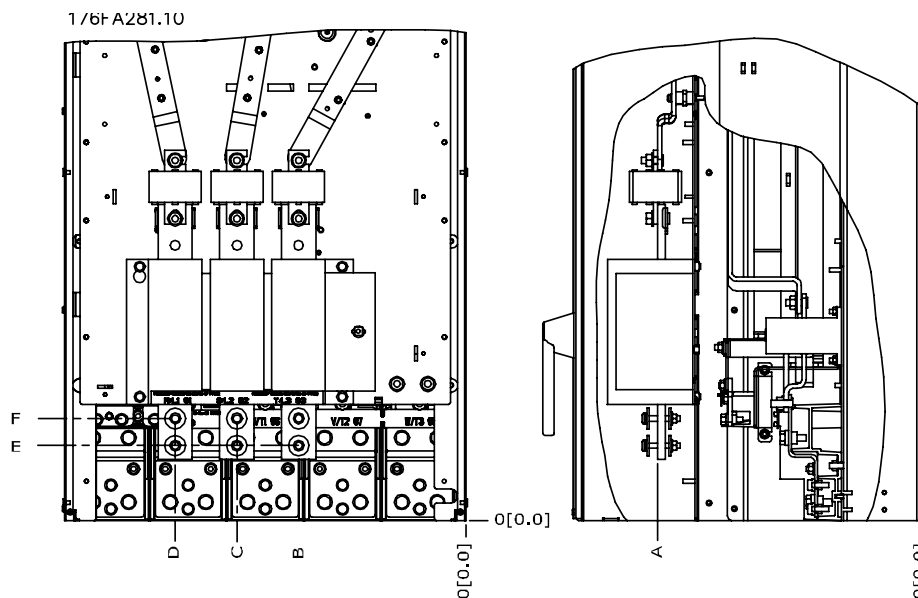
Posiciones de la conexión eléctrica del interruptor de desconexión en protección IP00
